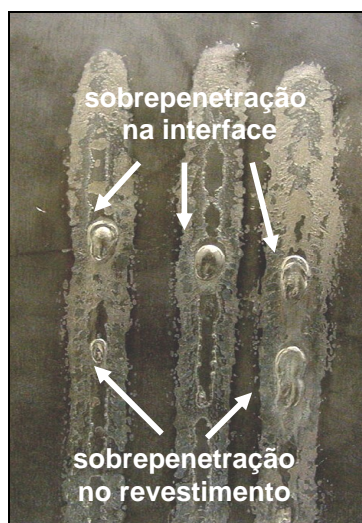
Vista da superfície inferior de chapa mostrando sobrepenetrações de cordões de solda depositados com 100 A de corrente sobre revestimento com 1,2 mm.
